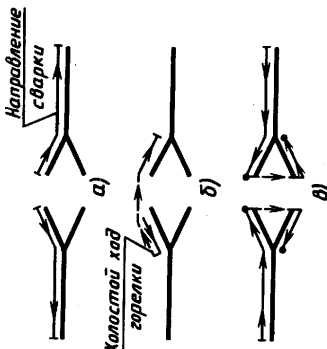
Схемы перемещения электродов по стыку при сварке: а, б — корневой шва; в — основного шва
